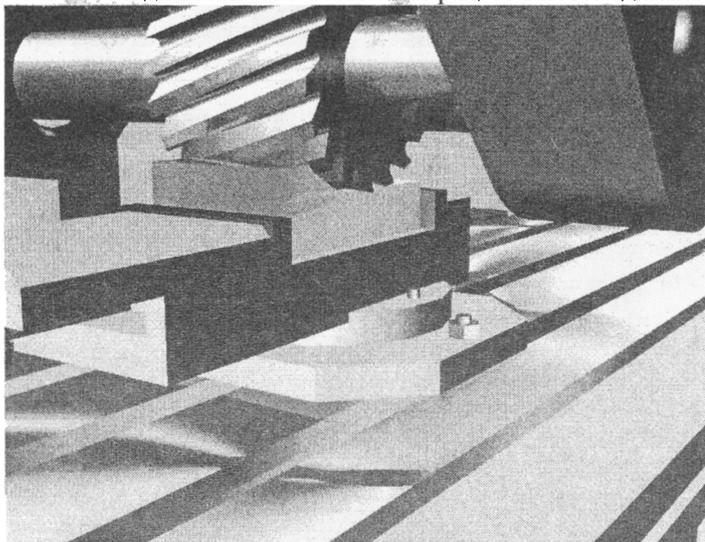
Фрезерование заготовки на горизонтально—фрезерном станке цилиндрической косозубой фрезой
